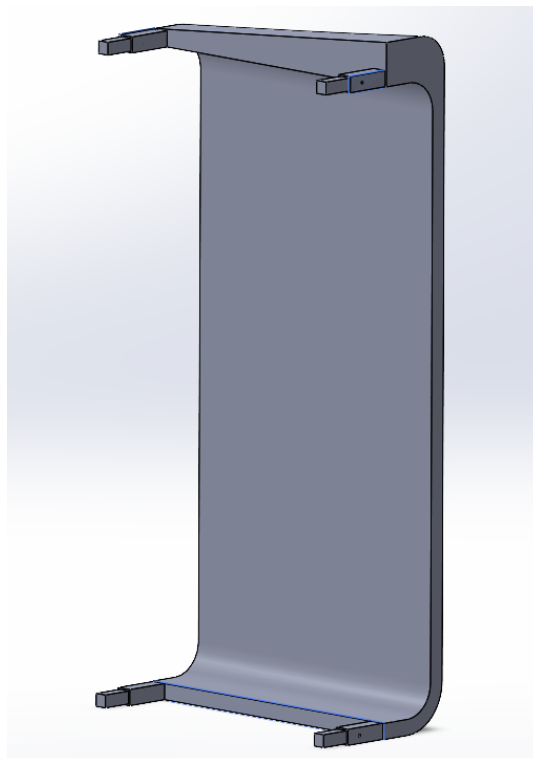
Estructura. Barra derecha C con su inclinación.
